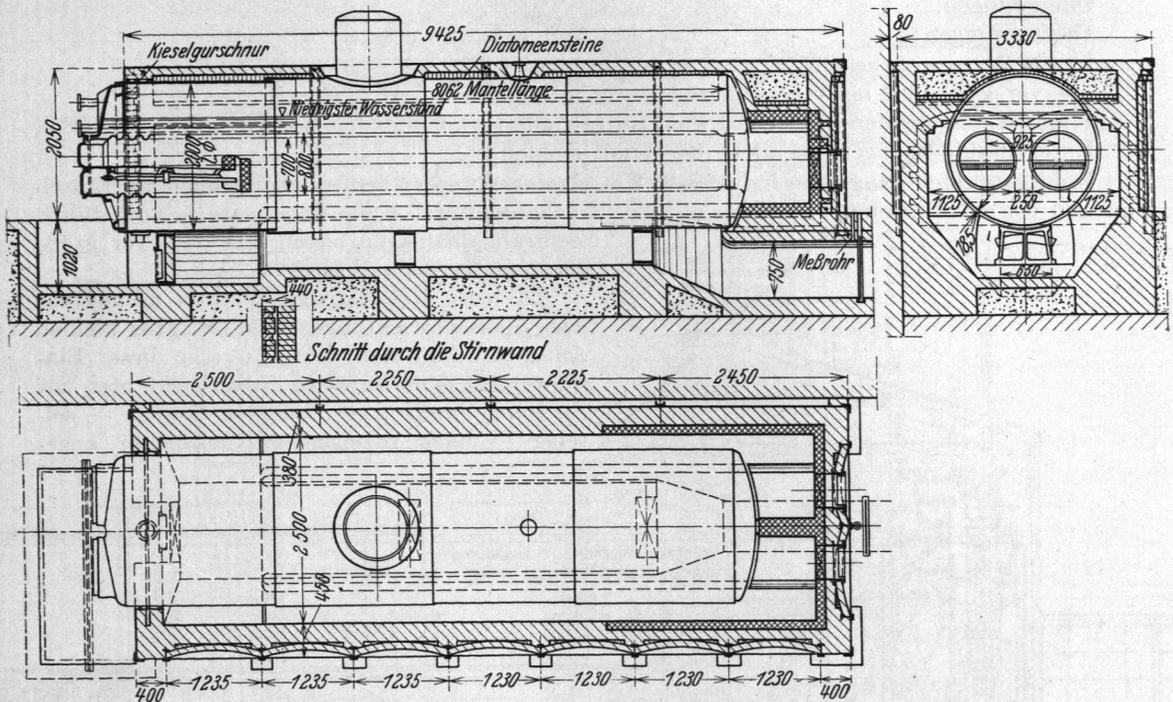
Zweiflammrohrkessel von 70 m² Heizfläche, 13 atü Betriebsdruck, mit Planrostfeuerung.
